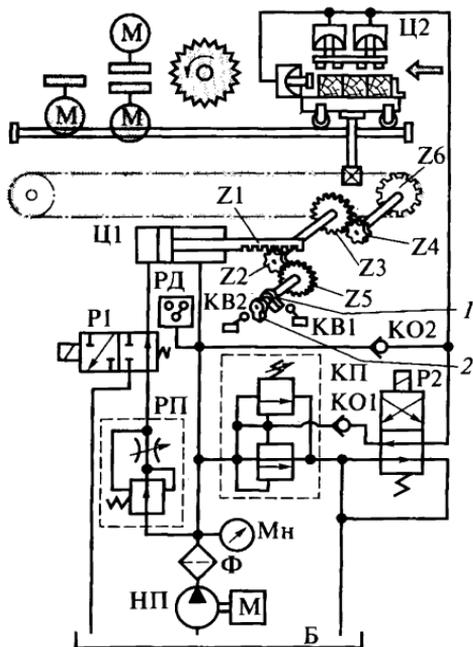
Гидрокинематическая схема одностороннего рамного шипорезного станка:
